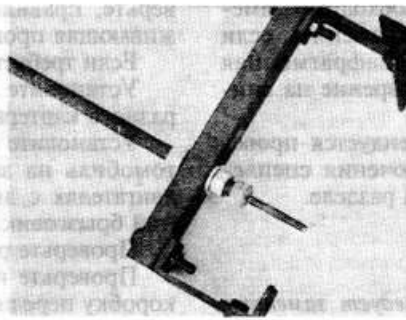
Самодельный инструмент для отсоединения ведущего вала коробки передач от сцепления
